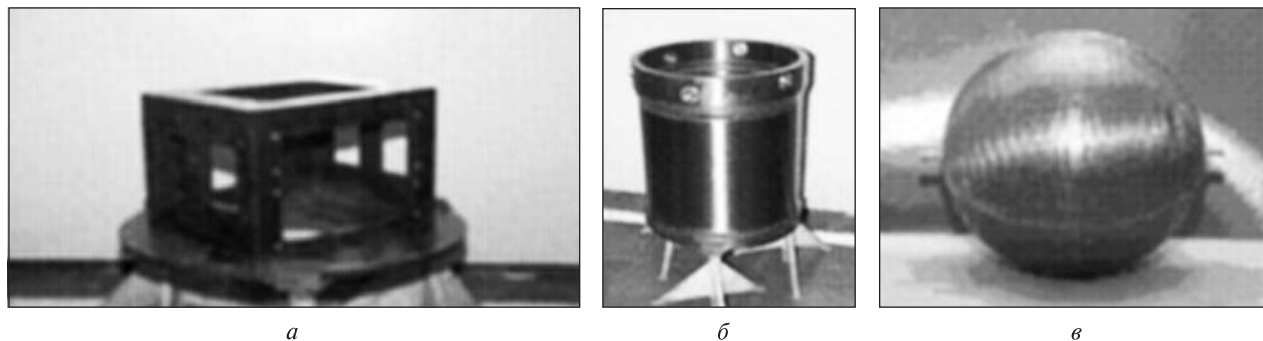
а — корпус объектива, б — тубус, в — металлопластиковый шаробаллон
